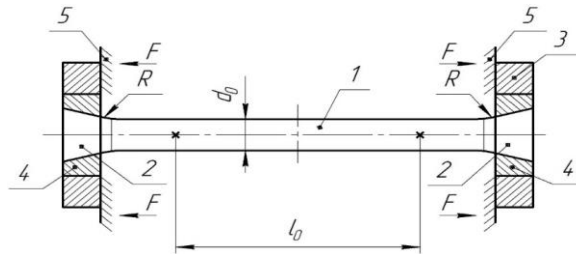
Устройство цилиндрического образца со съёмными заплечиками для испытания конструкционных материалов на растяжение: 1- образец; 2 – конические головки образца; 3 – бандажное кольцо съёмного заплечика; 4 – клинящее кольцо, разделённое на две или более частей, для обеспечения сборки; 5 – опорные поверхности, через которые образец нагружается силами F ; l_0 и d_0 соответственно расчётная длина (база) и диаметр рабочей части образца; R - радиус сопряжения конической и цилиндрической поверхностей.
